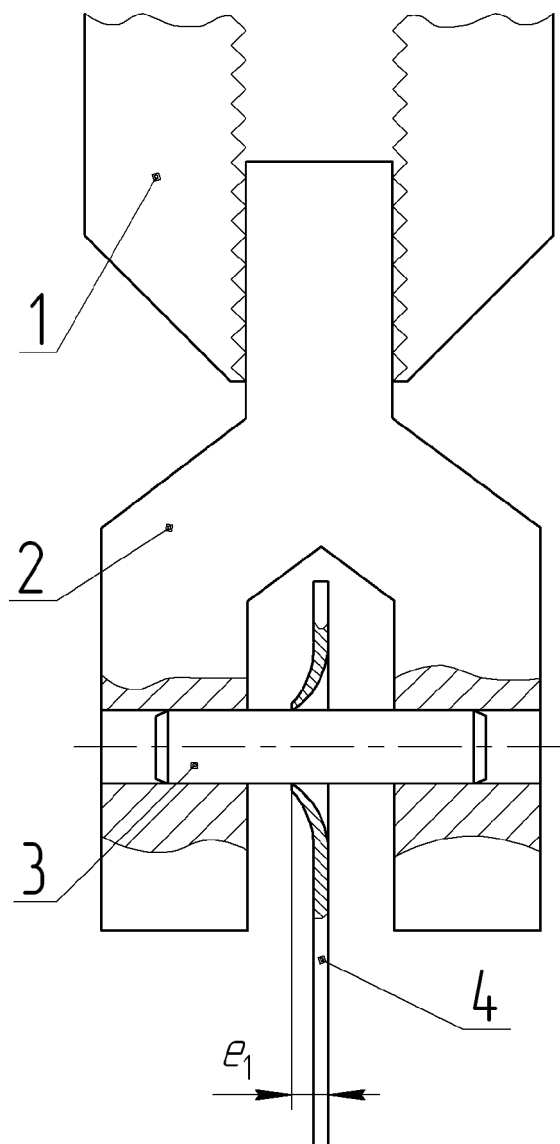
Коробление образца в процессе нагружения: 1) захваты машины; 2) вилка; 3) палец; 4) образец
